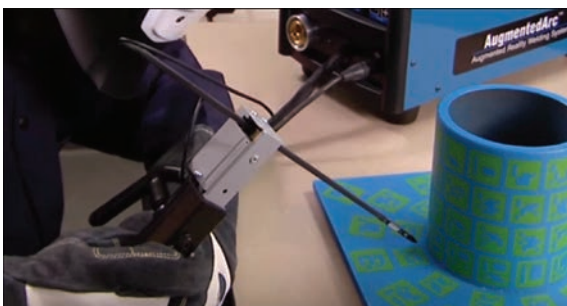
Виртуальная горелка MMA, имитирующая плавление электрода с его уменьшением в процессе сварки
